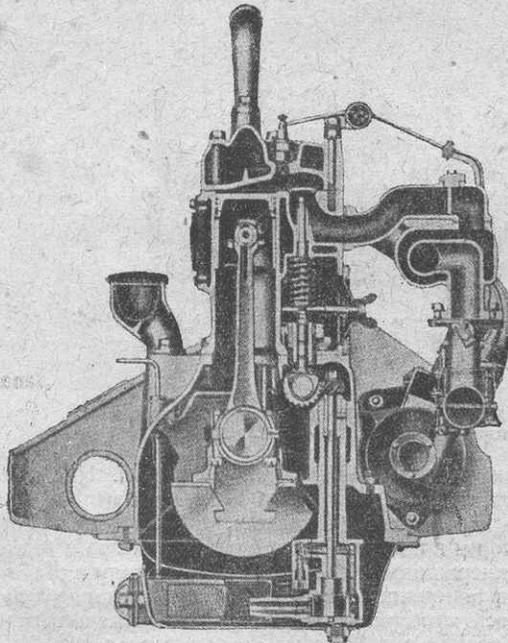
Поперечный разрез двигателя «Адлер», модель «Стандарт 8».
